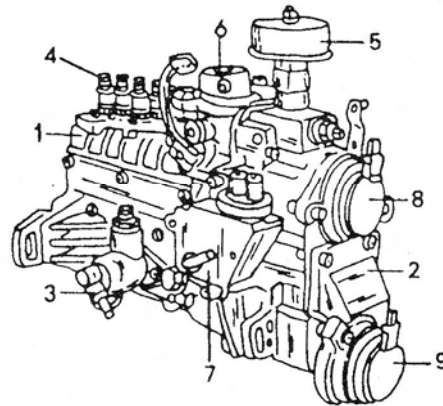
Топливный насос высокого давления с дополнительными устройствами
